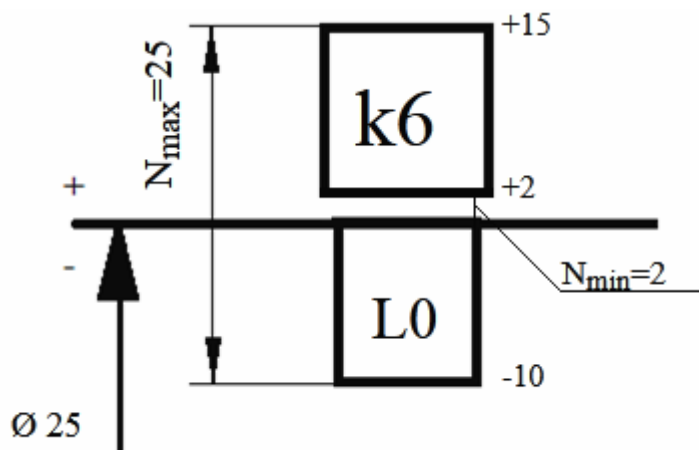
Поля допусков и показатели точности посадки для сопряжения внутреннего кольца подшипника и вала
